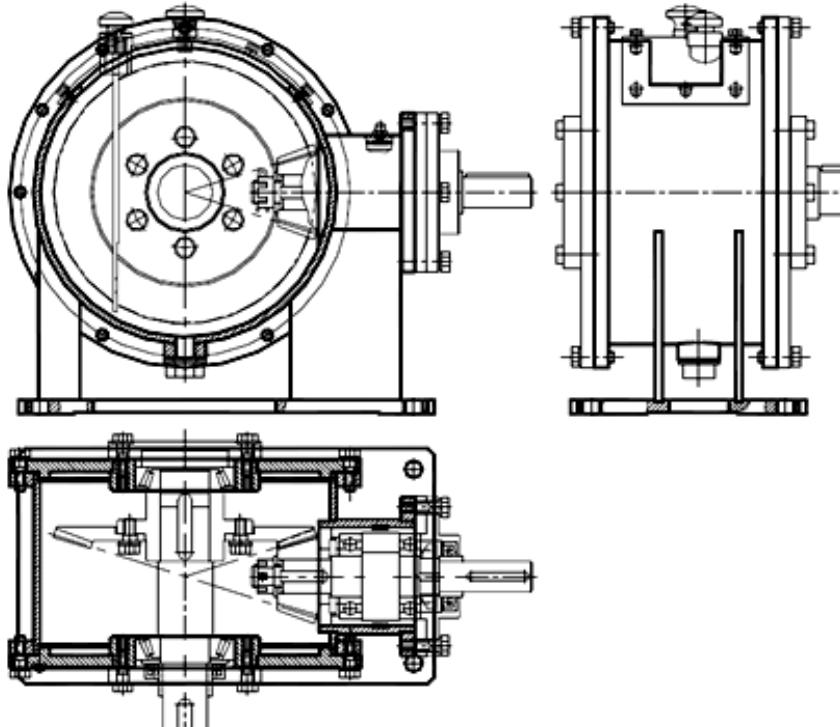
Зварний корпус конічного одноступінчастого редуктора
